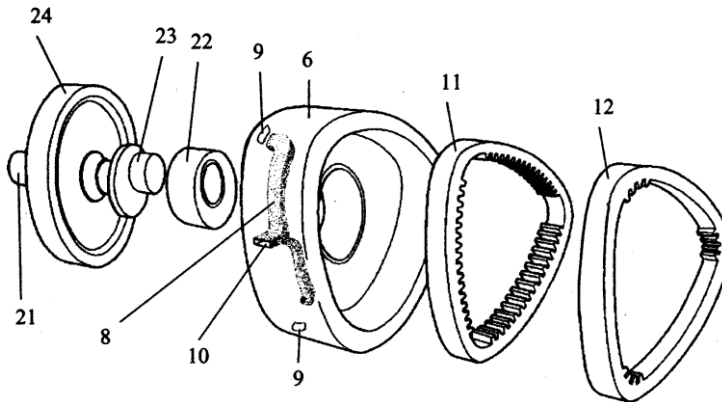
Конструкція ротора гарячої порожнини й механізму приводу вихідного вала.
